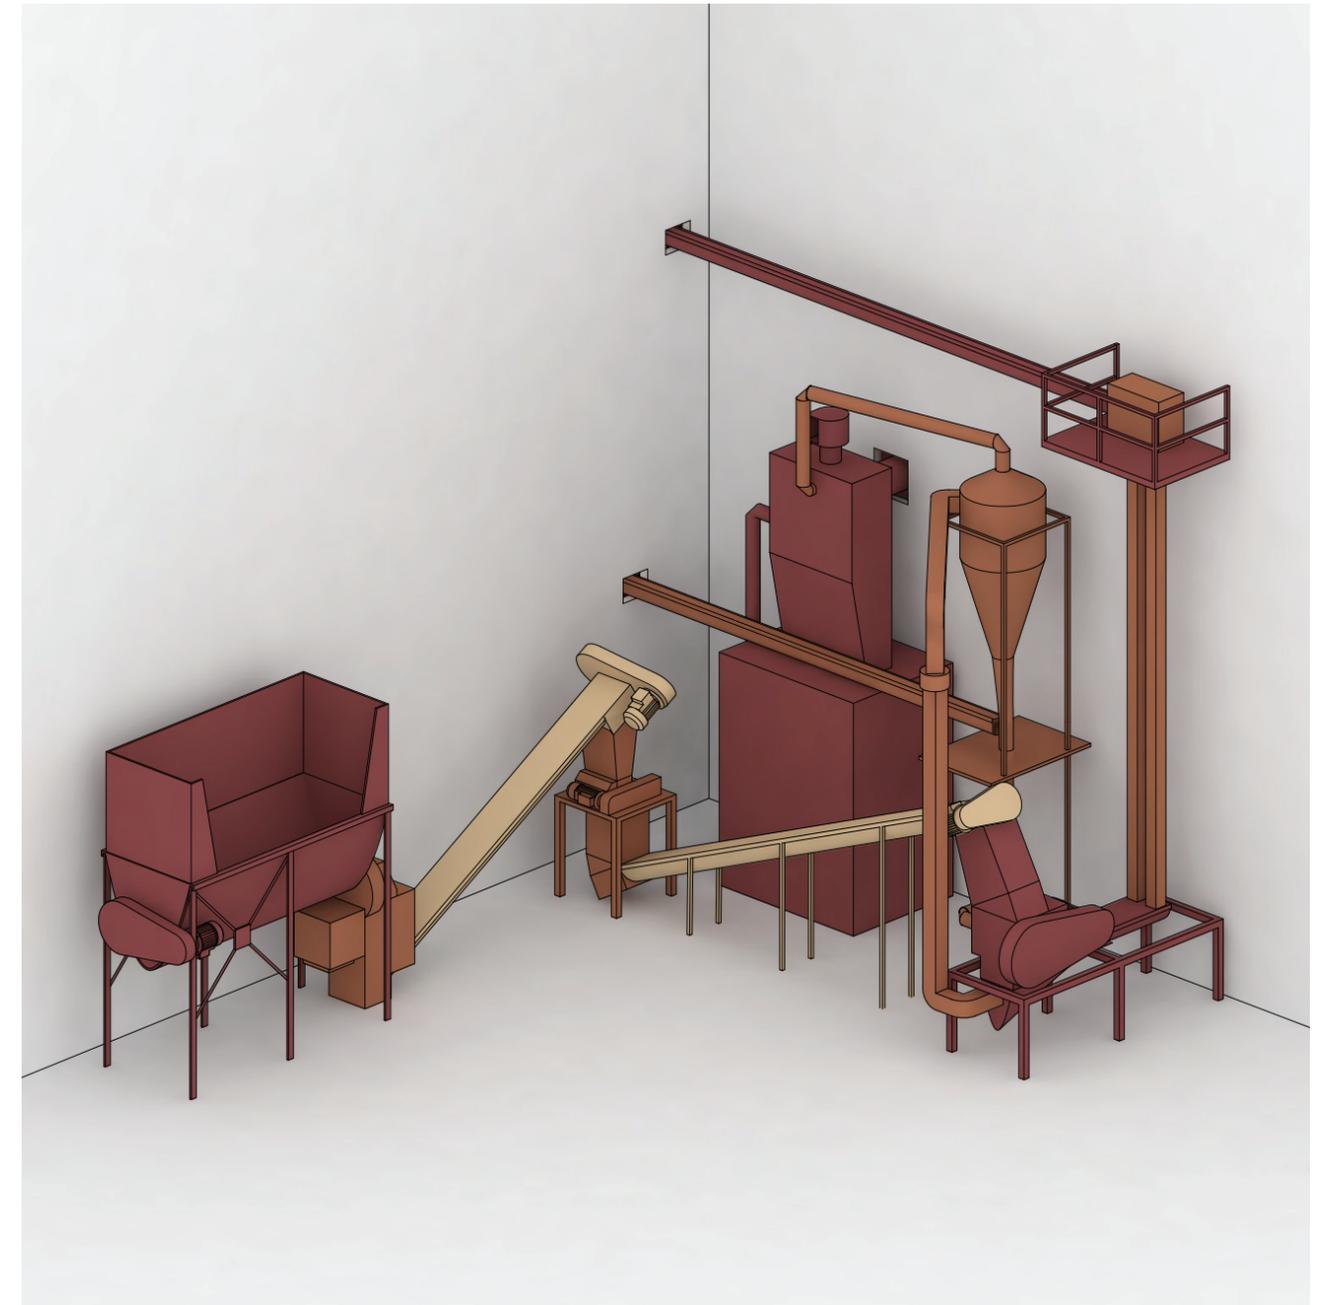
Modello 3D dell'impianto di frantumazione tutoli.
